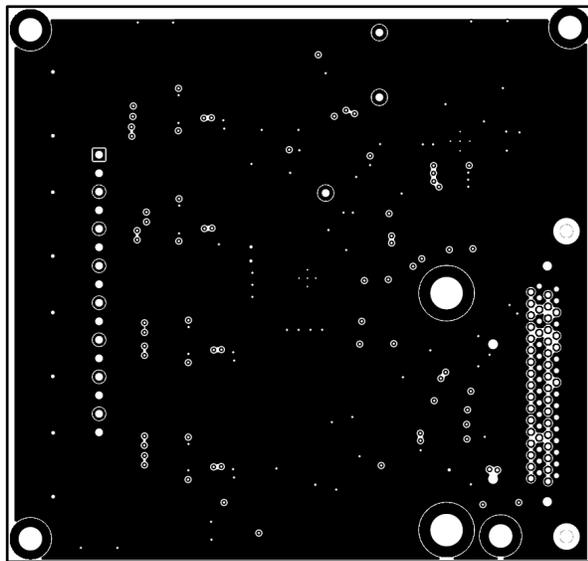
ADS8332EVMV2 PCB 第 2 层 : GND 层
